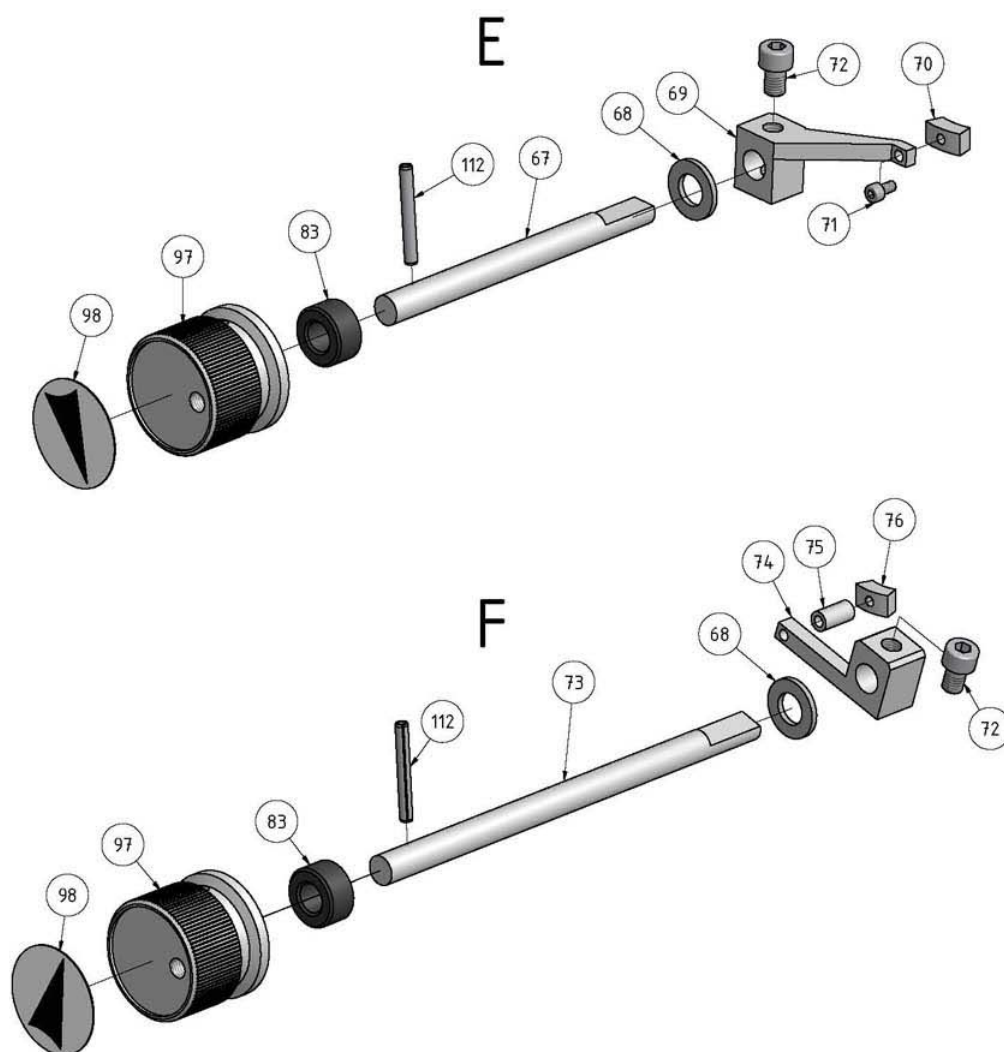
Fräskopf 4 von 6 - Cabezal fresador 4 de 6
